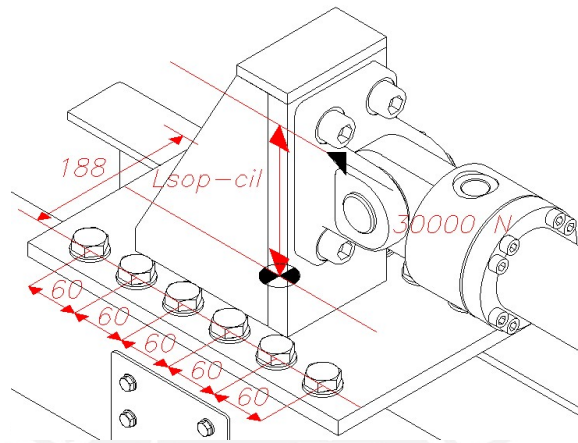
24. Fuerzas aplicadas sobre la unión atornillada del soporte de cilindro.
